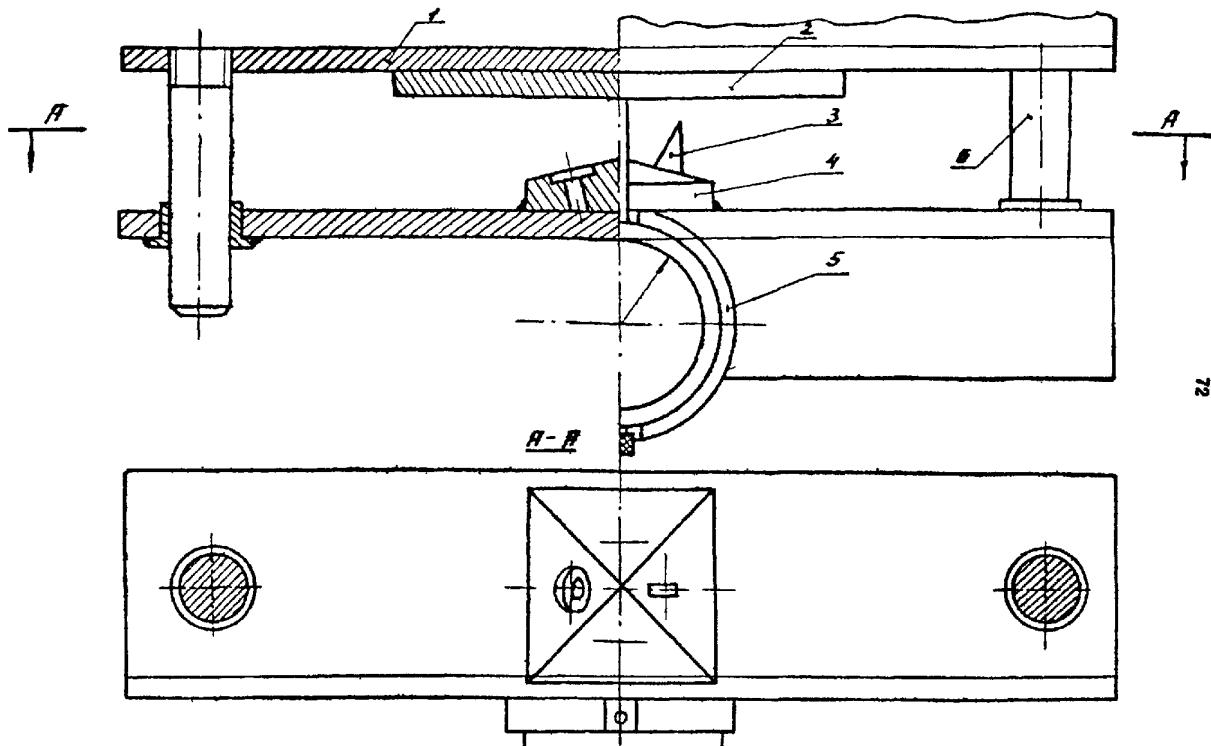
Устройство для нанесения зарубки способом вдавливания: 1 - уголок ; 2 - образец ; 3 - боек ; 4 - патрон ; 5 - оправка индикатора ; 6 - направляющая.
